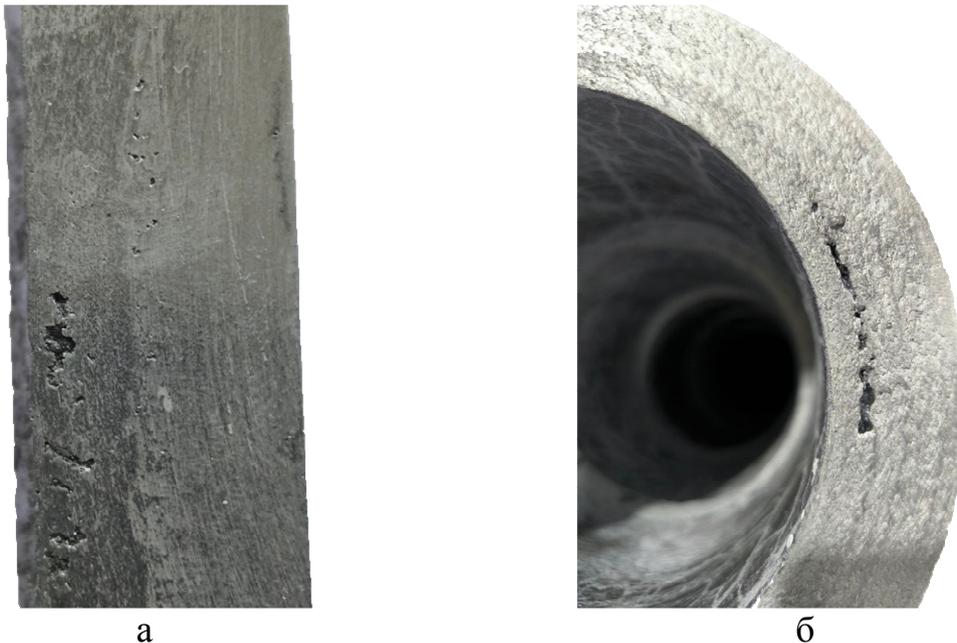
Продольный (а) и поперечный разрез (б) полый цилиндрической заготовки из силумина, полученной центробежным литьем
